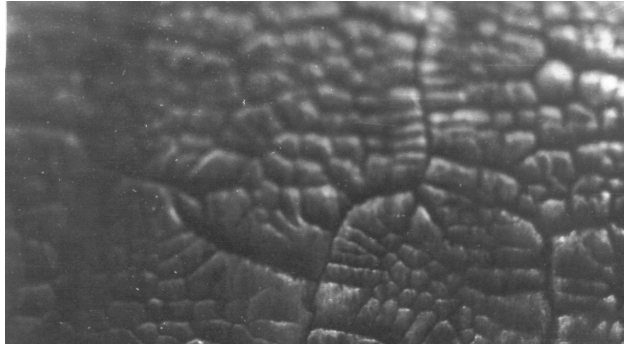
Сетка разгара на поверхности бочки валка слябинга 1150
